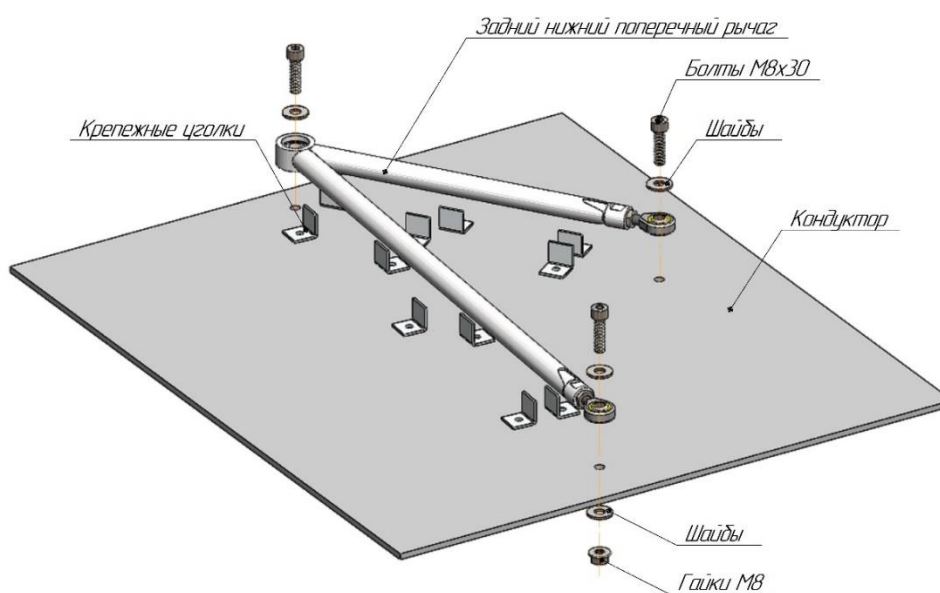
Установка элементов поперечного рычага на кондукторе, для последующей сборки
